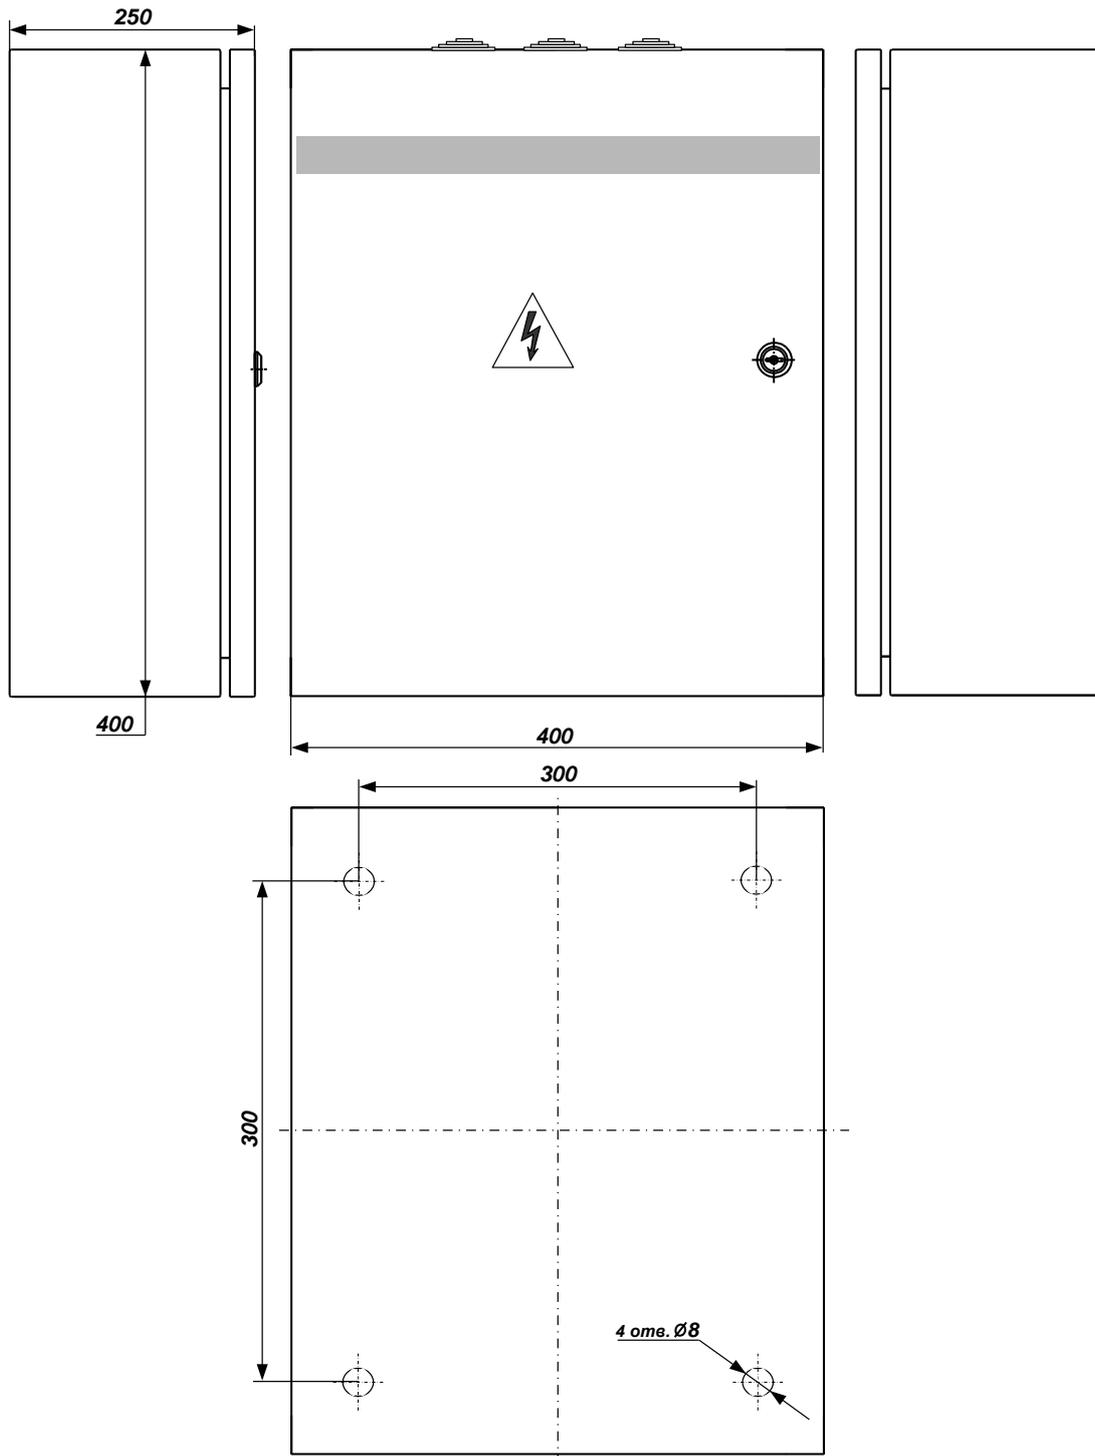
Внешний вид ППК-Р. Габаритные и присоединительные размеры
